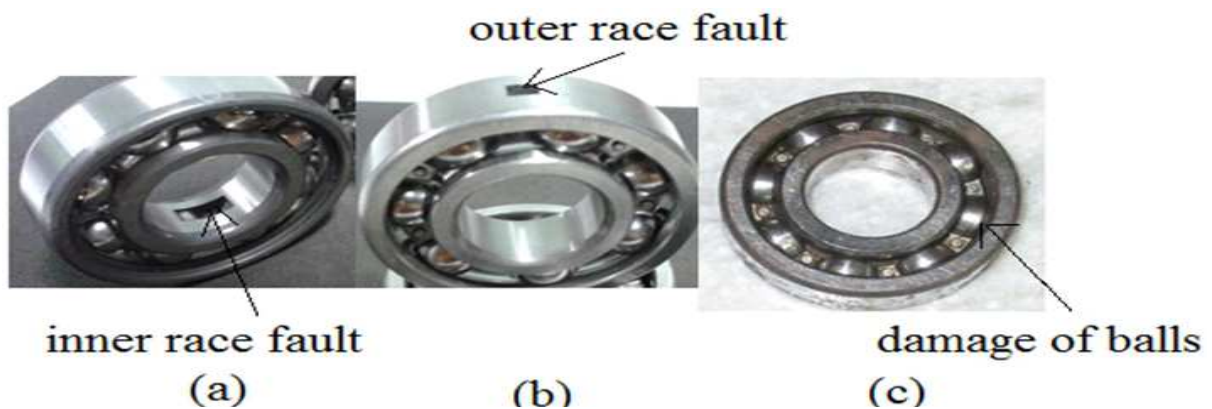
défauts de roulement: (a) bague interne, (b) bague externe, (c) défaut de la bille
